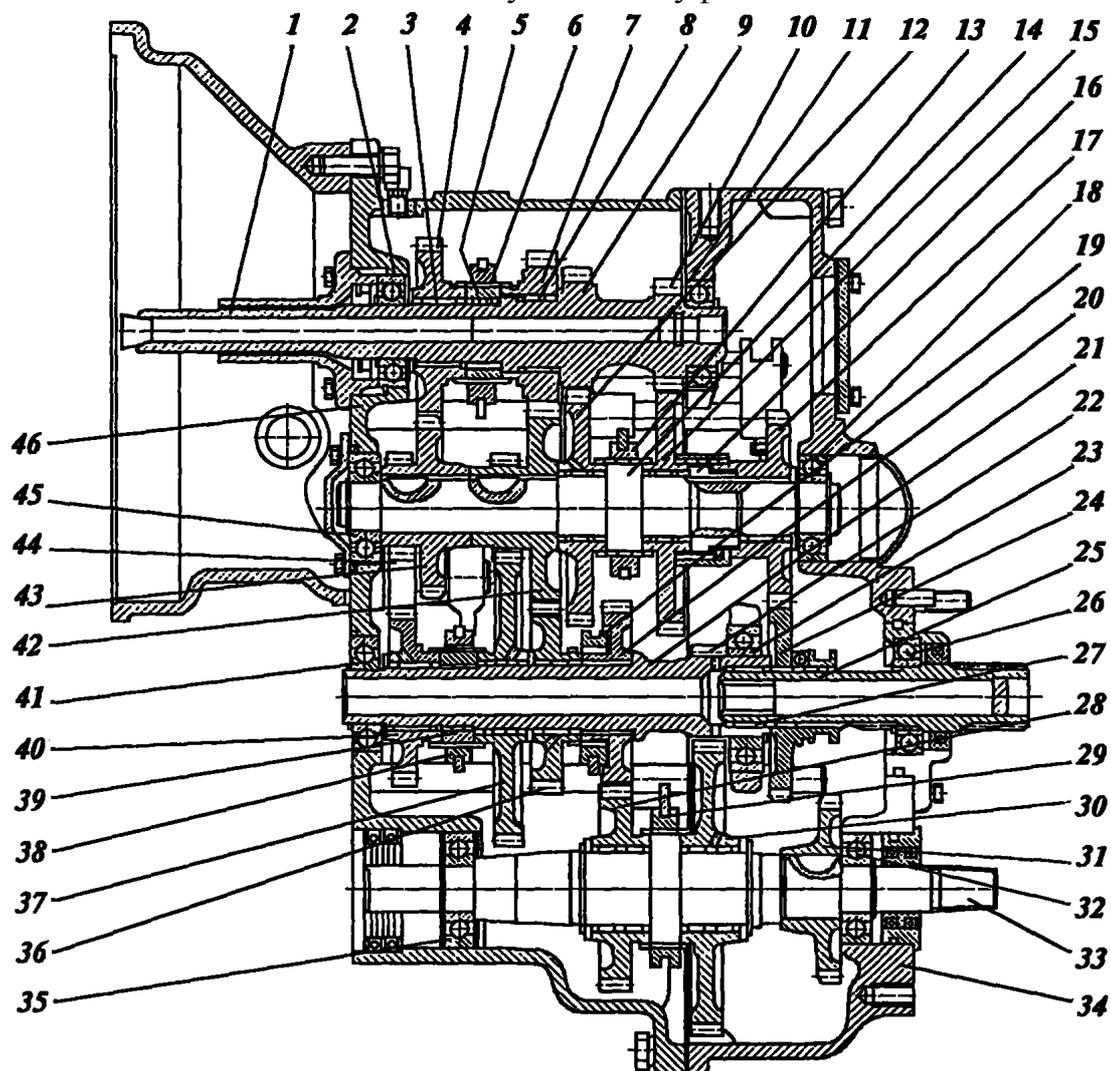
Коробка передач: 1 - первичный вал; 2, 11, 18, 23, 26, 32, 35, 41, 45 - подшипники; 3, 8, 27 - роликоподшипники; 4 - ведущая шестерня 4-й передачи; 5, 16, 39 - втулки; 6, 19, 29, 38 - муфты; 7 - ведущая шестерня 3-й передачи; 9 - зубчатый венец 2-й передачи; 10 - зубчатый венец 1-й передачи; 12 - ведомая шестерня 2-й передачи; 13 - муфта; 14 - первый промежуточный вал; 15 - ведомая шестерня 1-ой передачи; 17 - шестерня привода ВОМ; 20 - шестерня; 21 - запорный промежуточный вал; 22 - зубчатый венец понижающего редуктора; 24 - шестерня привода ВОМ; 25 - вал привода ВОМ; 28 - ведомая шестерня понижающего редуктора; 30 - ведомая шестерня повышающего редуктора; 31 - шестерня синхронного привода ВОМ; 33 - выходной вал; 34 - корпус КПП; 36 - ведомая шестерня II диапазона; 37 - ведомая шестерня I диапазона; 40 - ведомая
